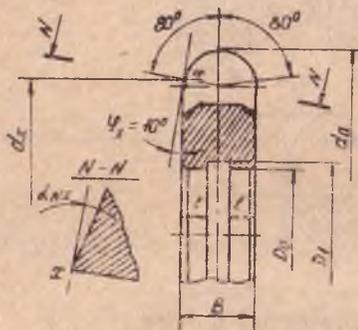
Задний угол в нормальном сечении для боковой точки режущей кромки
